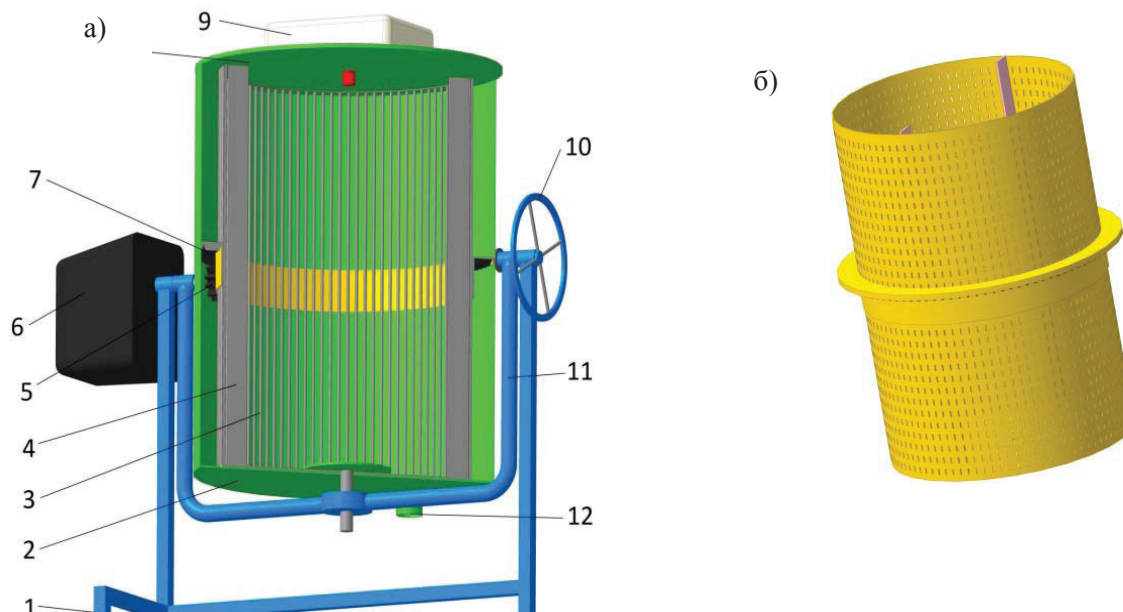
Сверхвысокочастотная установка с цилиндрическим барабаном-резонатором для периодического режима работы: а) общий вид в разрезе; б) перфорированная резонаторная камера с зубчатым венцом; 1 – монтажная рама на колёсах; 2 – цилиндрический экранирующий корпус; 3 – цилиндрический резонатор; 4 – внутренние рёбра; 5 – ведущая шестерня; 6 – мотор-редуктор; 7 – зубчатый венец; 8 – крышка экранирующего корпуса; 9 – генераторный блок с магнетроном и излучателем; 10 – механизм для застопоривания установки; 11 – поворотная рама для опоры и изменения угла наклона установки; 12 – сливной патрубок
